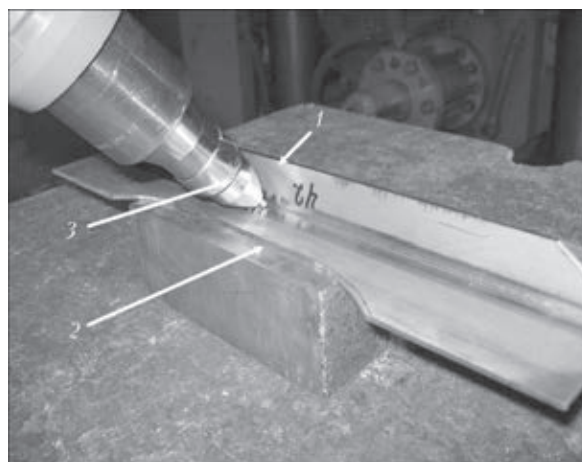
Обработка таврового сварного соединения образца из сплава ВТ20 ручным ударным инструментом по технологии ВМП: 1 — образец; 2 — подкладка; 3 — рабочая головка ударного инструмента
